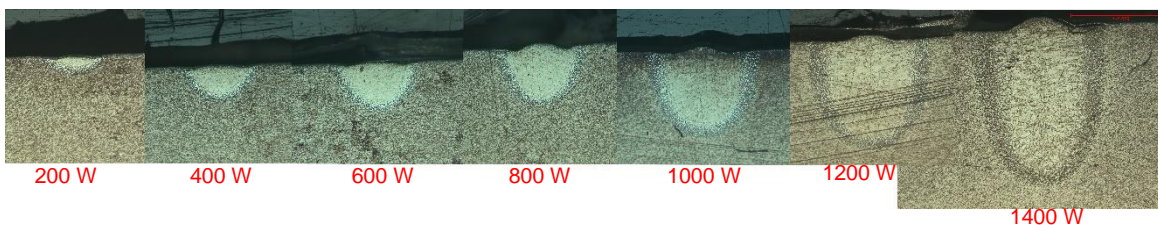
Cordões de soldadura com laser contínuo com potência de 200, 400, 600, 800, 1000, 1200 e 1400W da esquerda para a direita.
